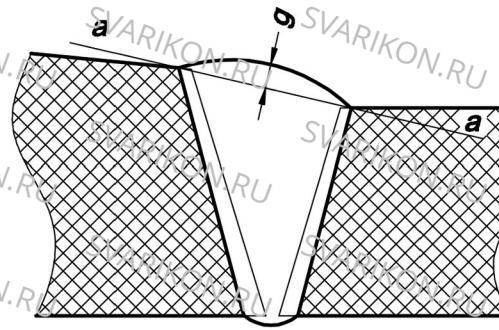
Измерение избыточного материала стыкового сварного шва ( $g$ ) при различном уровне наружных поверхностей деталей, вызванном разницей в толщинах стенок.
